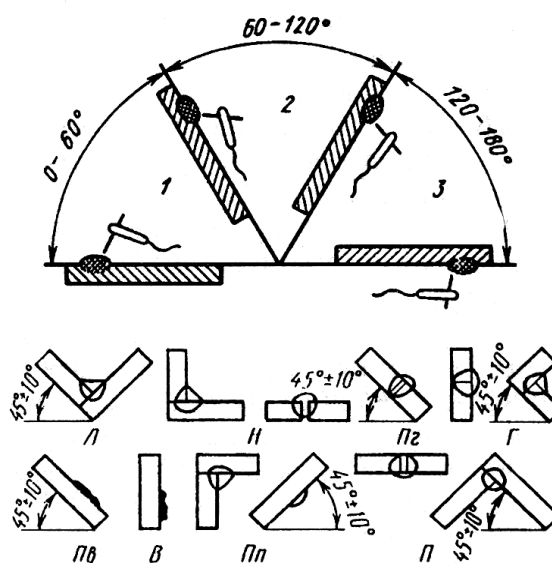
Основные положения сварки и их обозначения: 1 – нижнее; 2 – вертикальное или горизонтальное; 3 – потолочное
